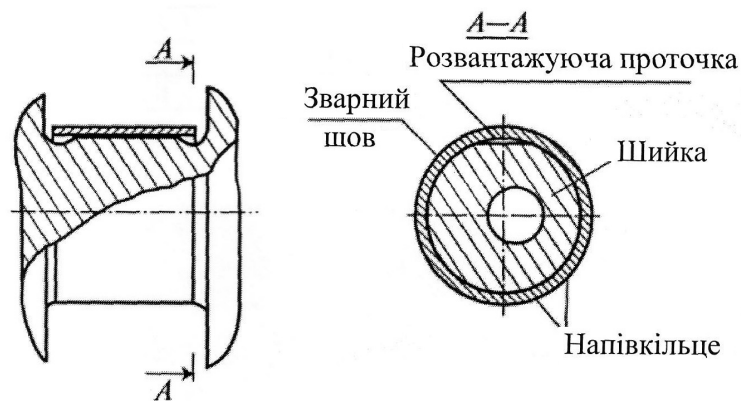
Схема відновлення шийок колінчастого валу двигуна ЗМЗ-511 приварюванням сталевих півкільць
